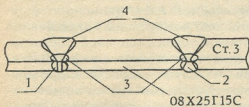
Сварка полос биметалла: 1 - корень шва V-образной канавки, сварка АДС; 2 - корень шва X-образной канавки, сварка ЭДС; 3 - переходные зоны, сварка ЭДС (эл. ОЗЛ-17У); 4 - основной металл Ст. 3, сварка ЭДС (эл. УОНИ-13/55)
